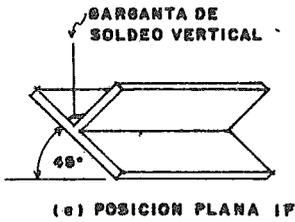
POSICIONES DE PLACAS A EXAMINAR PARA SOLDEO EN FILETE
